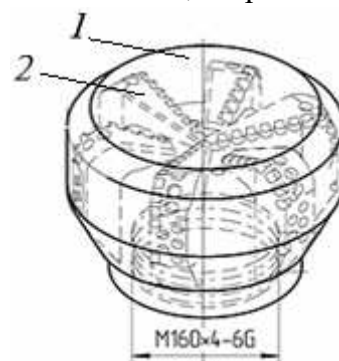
Совмещенный общий вид цельнометаллической заготовки корпуса долота после комплексной токарной (1) и фрезерной обработки (2) на станках с ЧПУ
